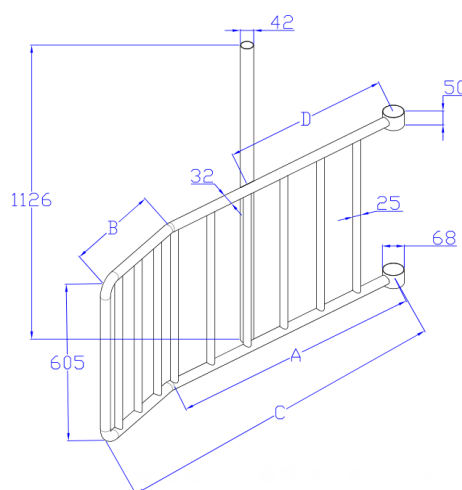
Puerta de entrada. Anexo A Plano 18 a Plano 21
